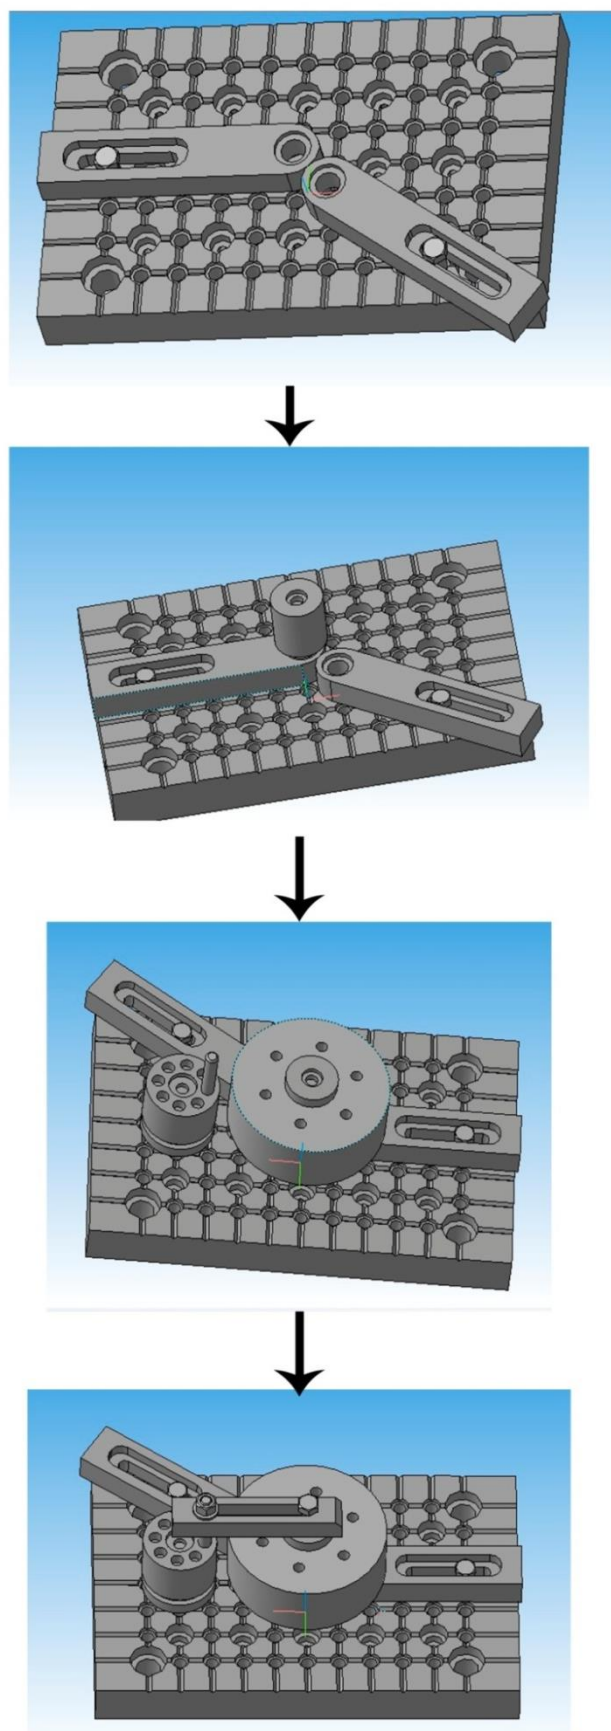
Пошаговый процесс сборки приспособления УСПО
